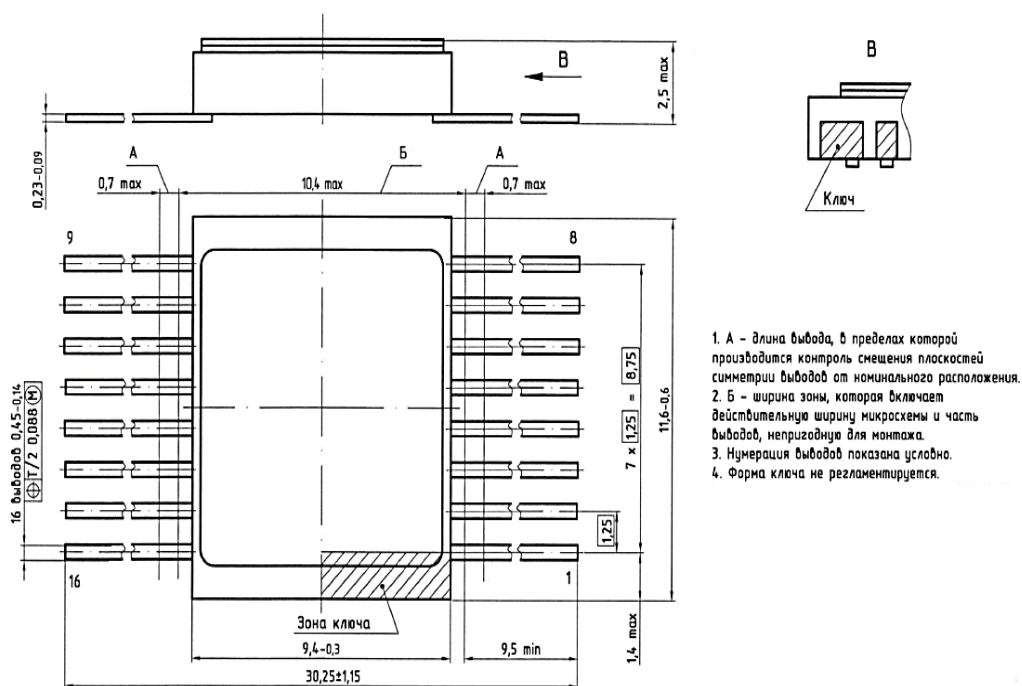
Габаритный чертеж корпуса 402.16-18 (размеры в мм)
